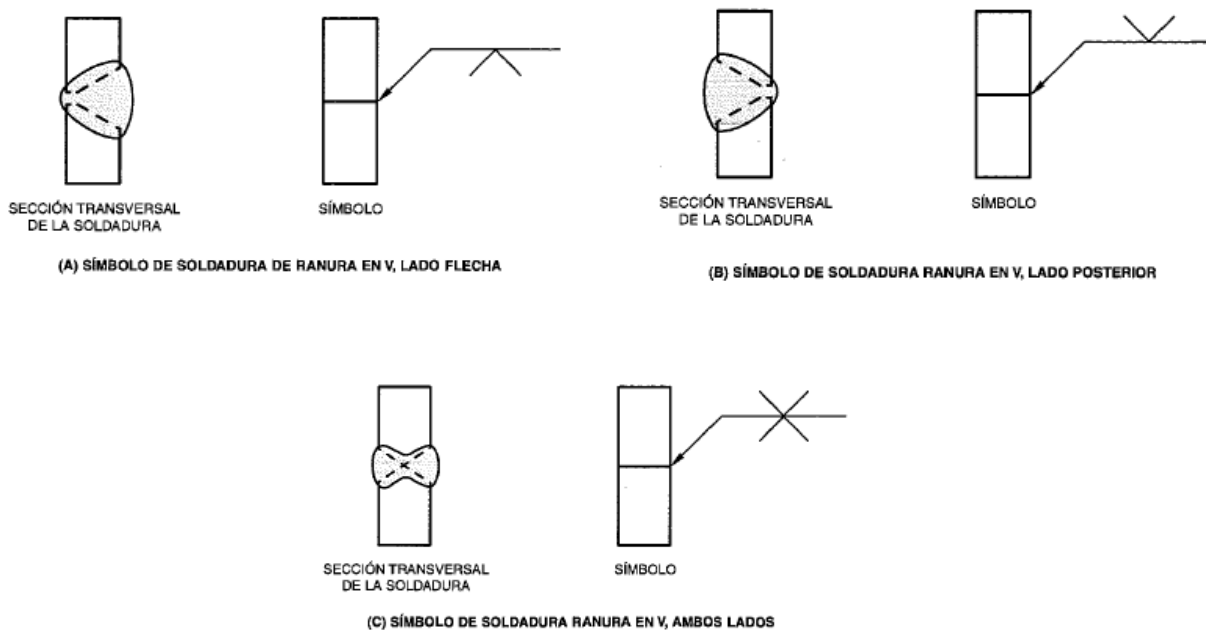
Aplicación de símbolos de soldadura. [15]
